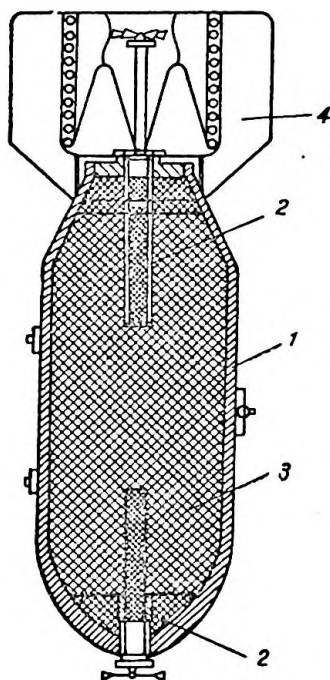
Bombă explozivă de aviație cu destinație generală:
